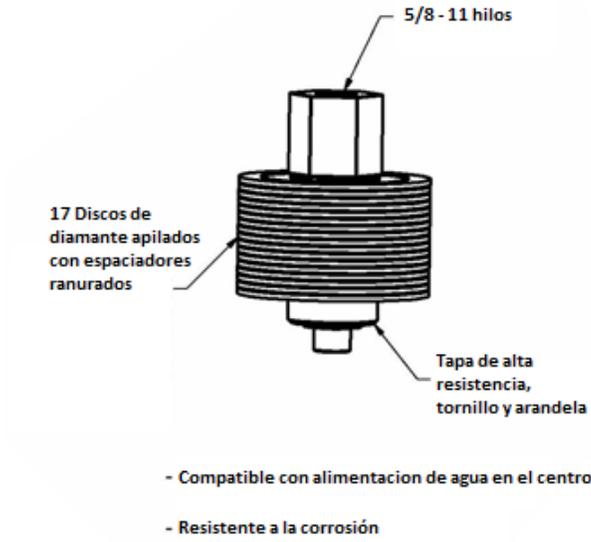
RapidZ™-CORTE (ensamblado)
